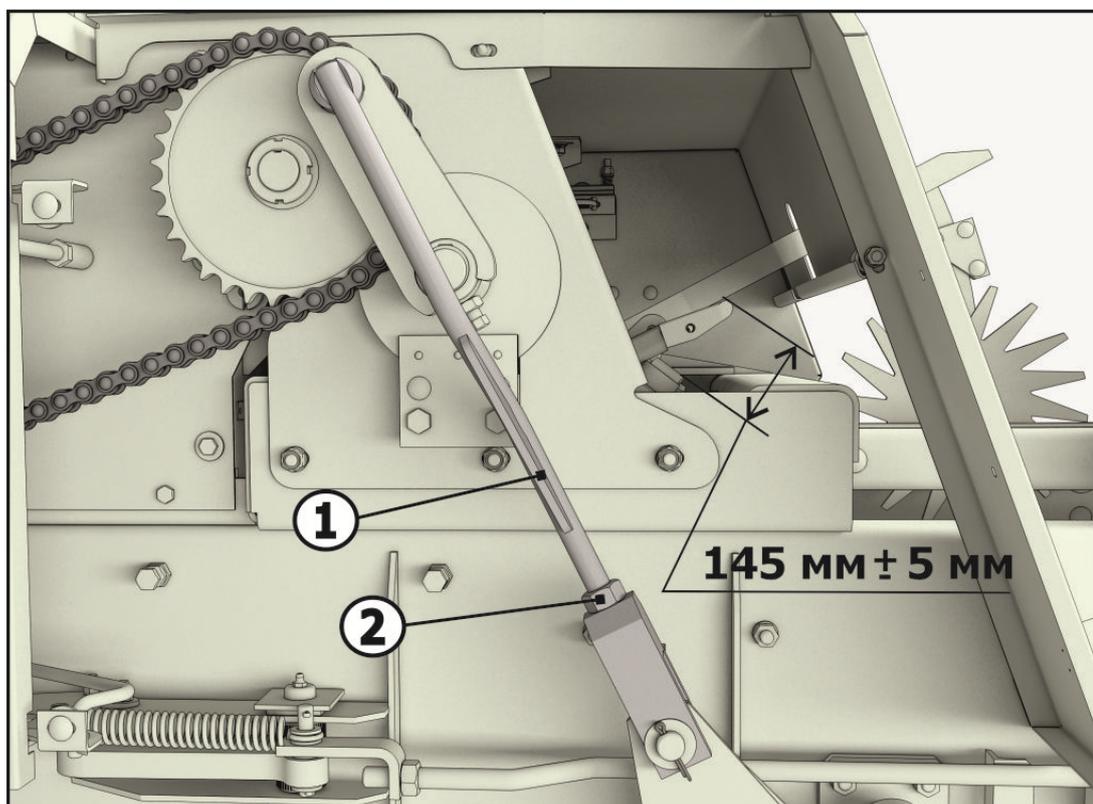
Регулировка положения зубчатого колеса обвязывающего узла
